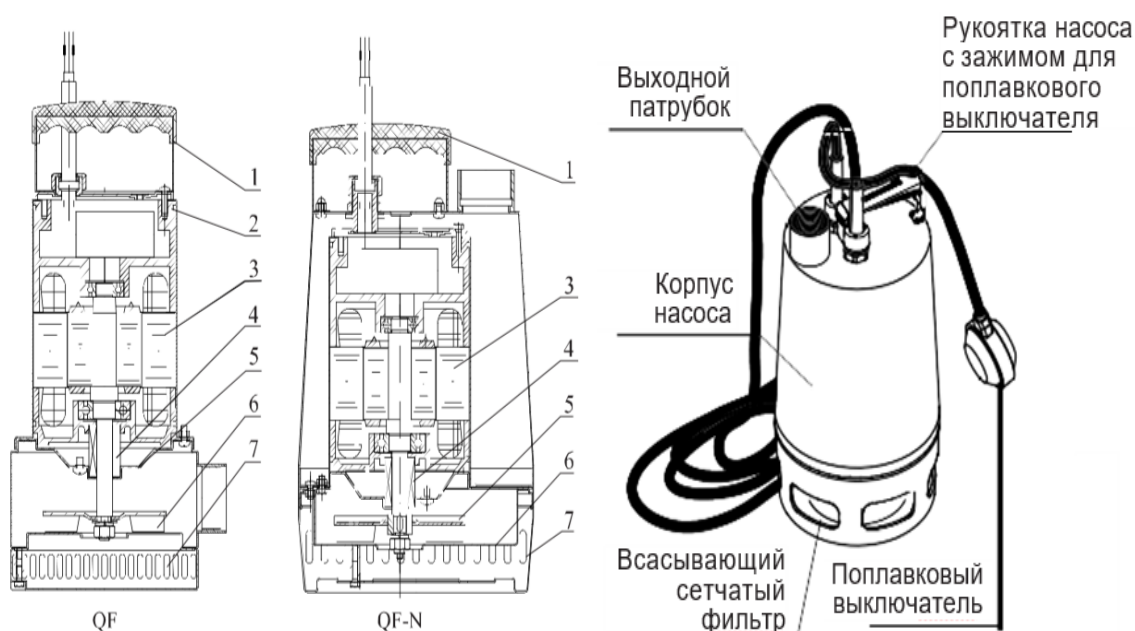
Схема расположения патрубков насоса и вид насоса в разрезе
